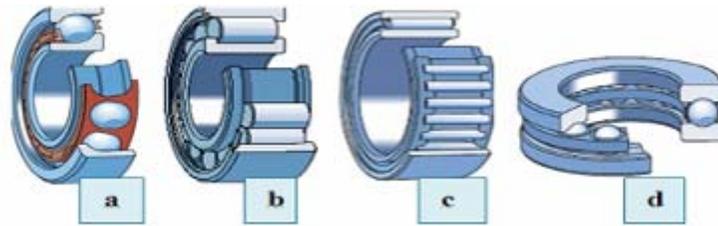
Diferentes tipos de rodamientos. a) Radial De bola, b) De Rodillo, c) De aguja, d) Rodamiento axial. [5]
